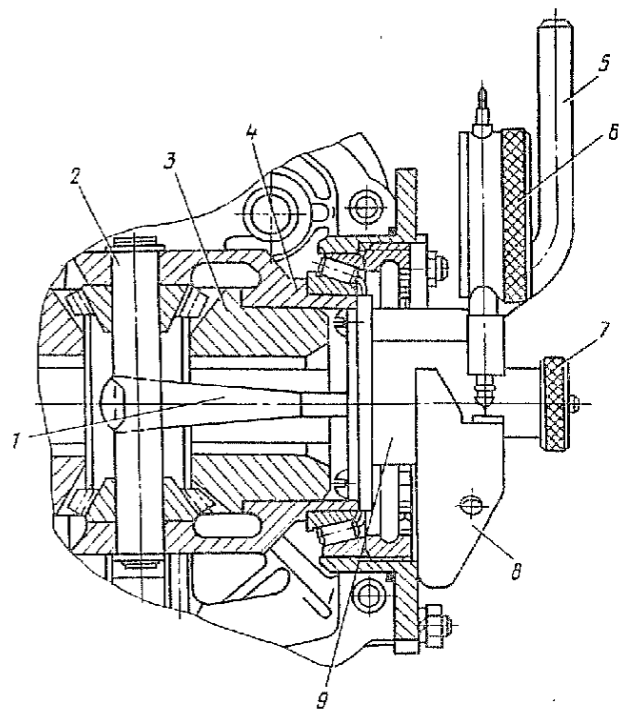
Контроль бокового зазора в зацеплении шестерен главной передачи в редукторе заднего моста и коробке передач:
